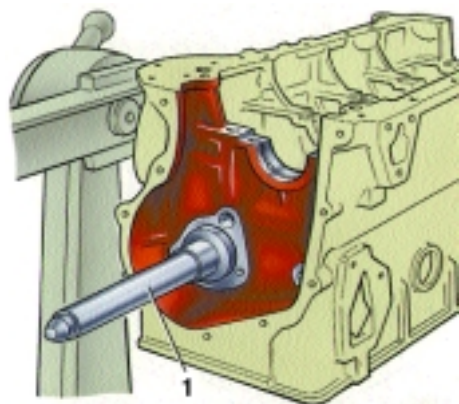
Снятие и установка втулки валика привода масляного насоса двигателя мод. 2106-70: 1 – оправка
